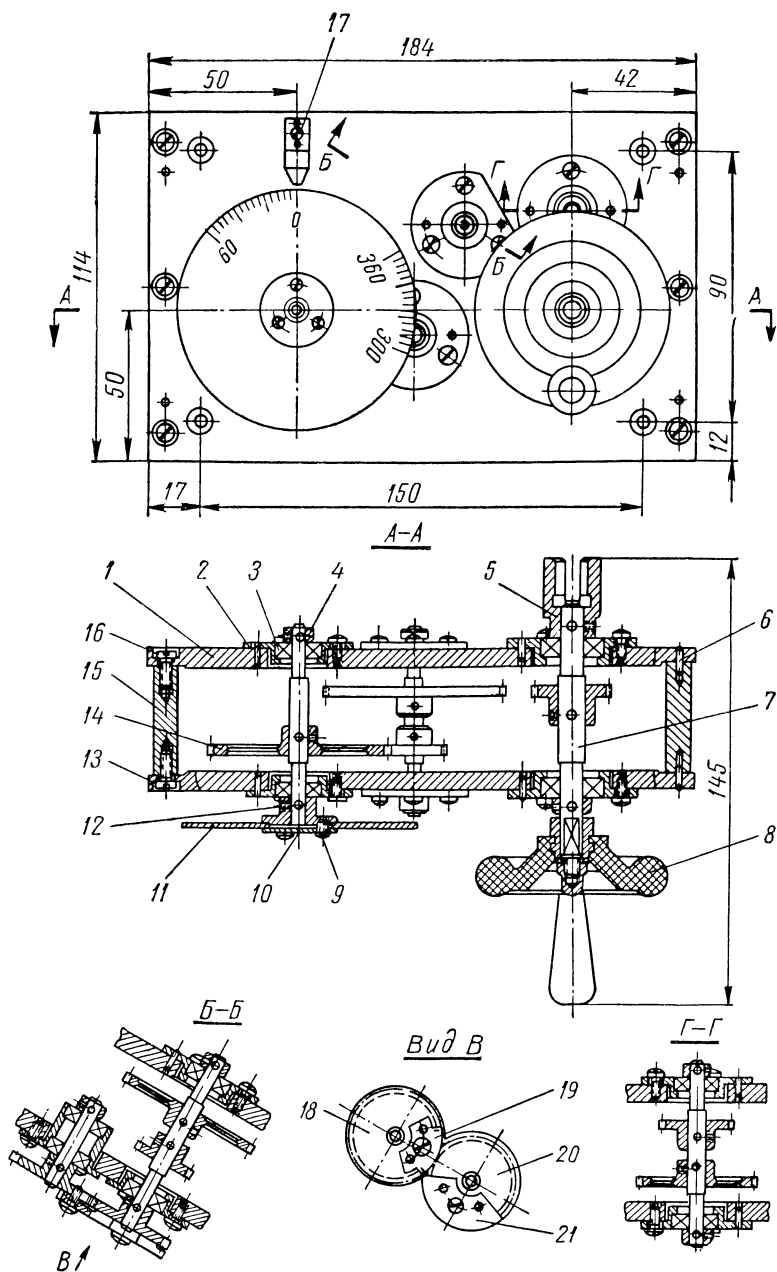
Двухплатная конструкция механизма ручного ввода математической величины
